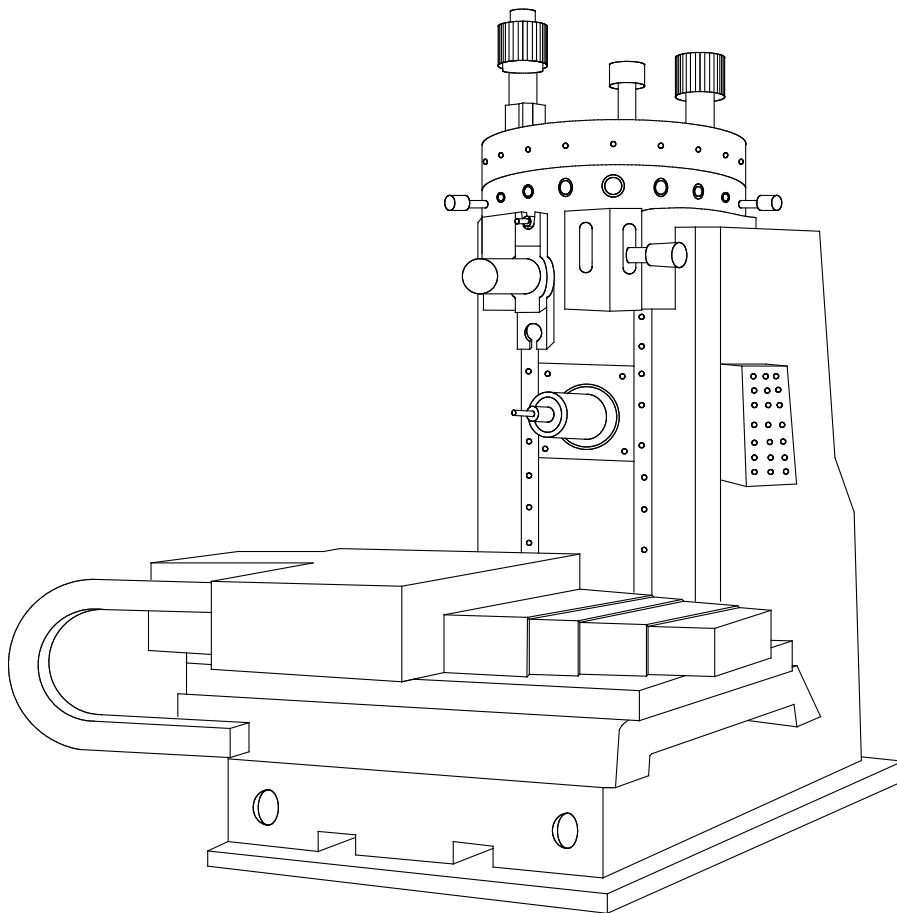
Багатоопераційний верстат 2А622-МФ2
